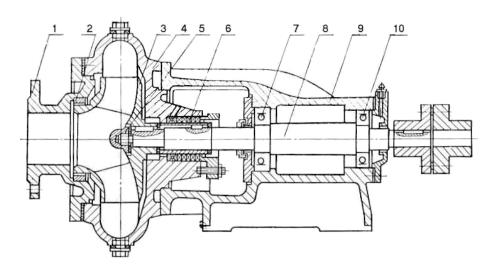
Схема насоса СД: 1 — всасывающий патрубок; 2 — уплотнительное кольцо рабочего колеса; 3 — рабочее колесо закрытого типа; 4 — корпус; 5 — крепежная гайка рабочего колеса; 6 — защитная втулка вала; 7, 10 — подшипники качения; 8 — вал; 9 — кронштейн
